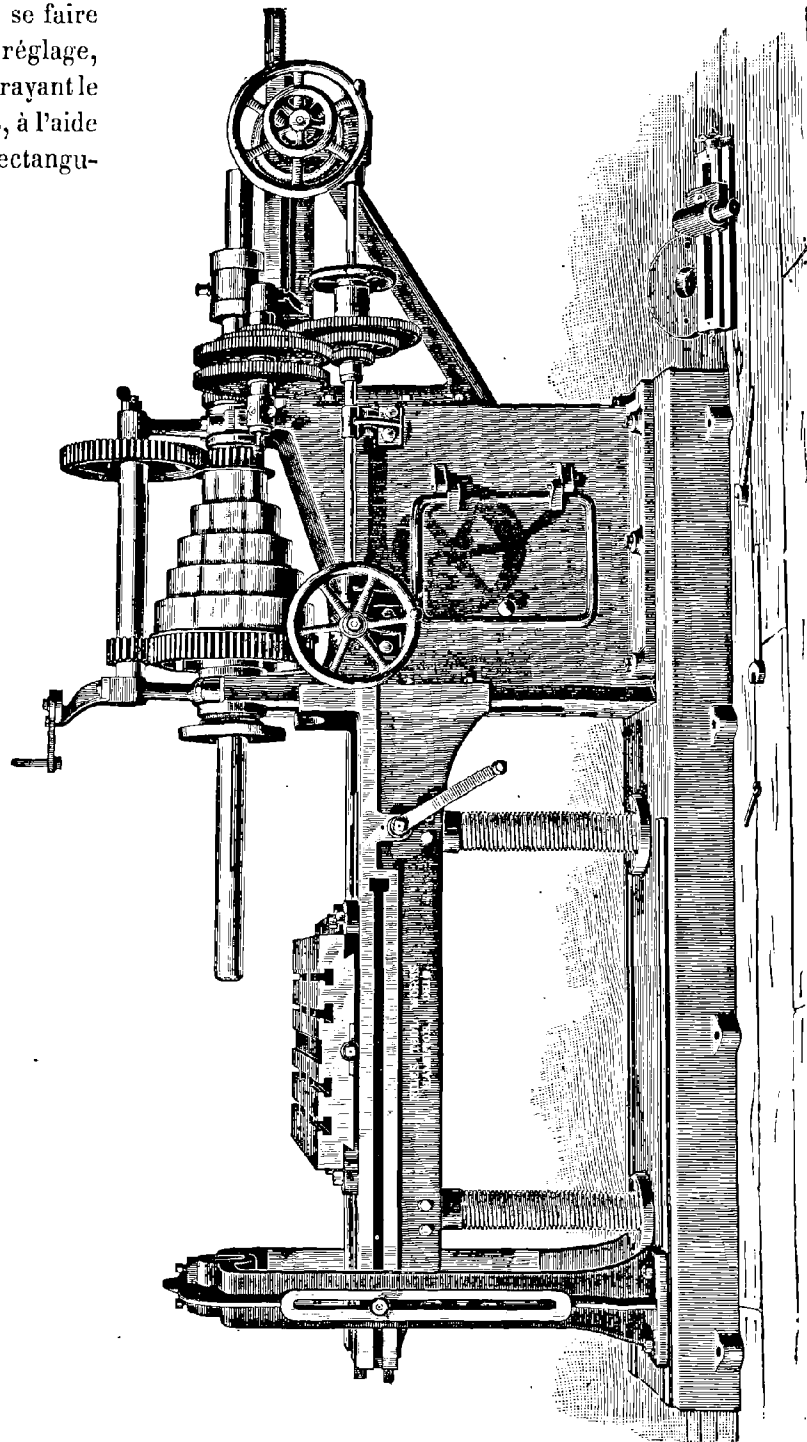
Machine horizontale à percer, aléser et surfacer Niles.
